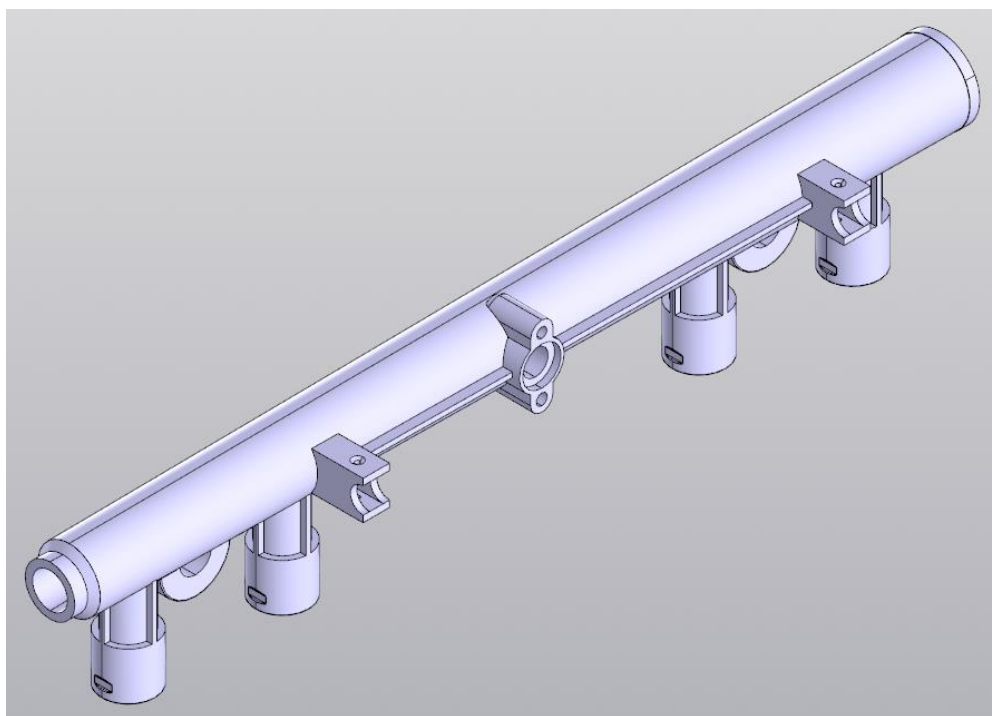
3D модель корпуса топливной рампы (вид спереди)
